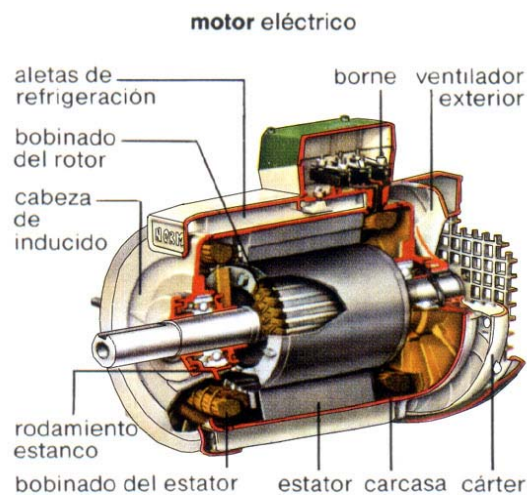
MOTOR DE ROTOR EN CORTOCIRCUITO
